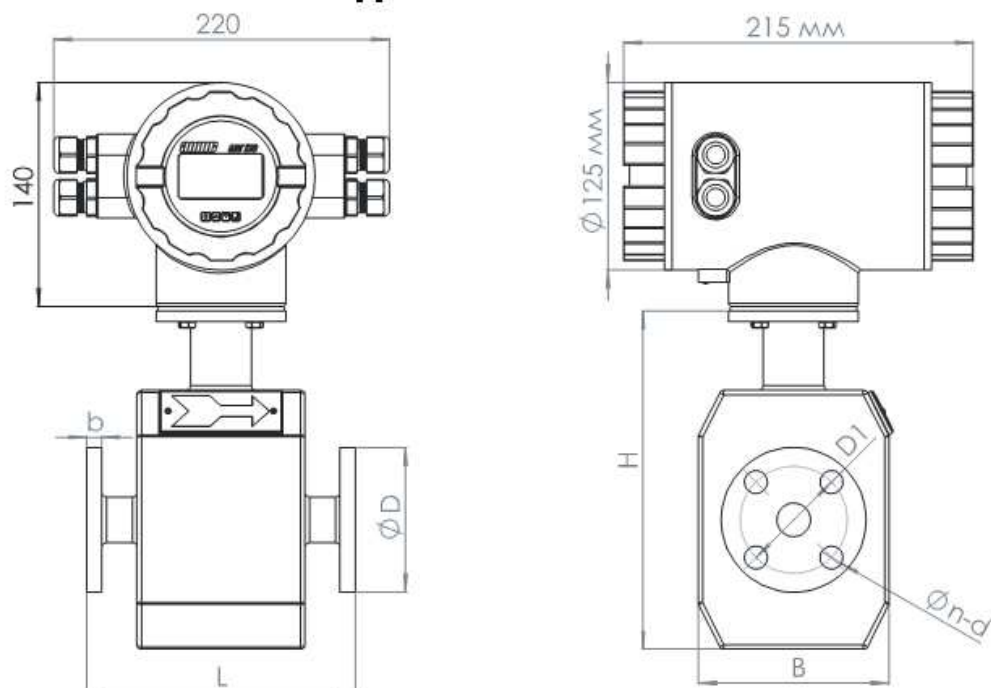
Габаритные и присоединительные размеры расходомера (Ду 15 - 80мм)
